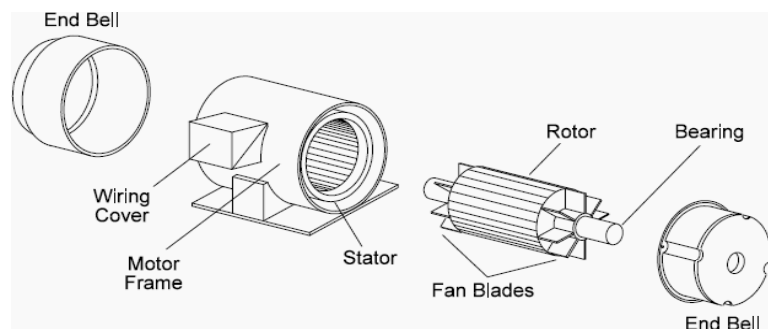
Konstruksi detail motor induksi dengan "rotor belitan"
